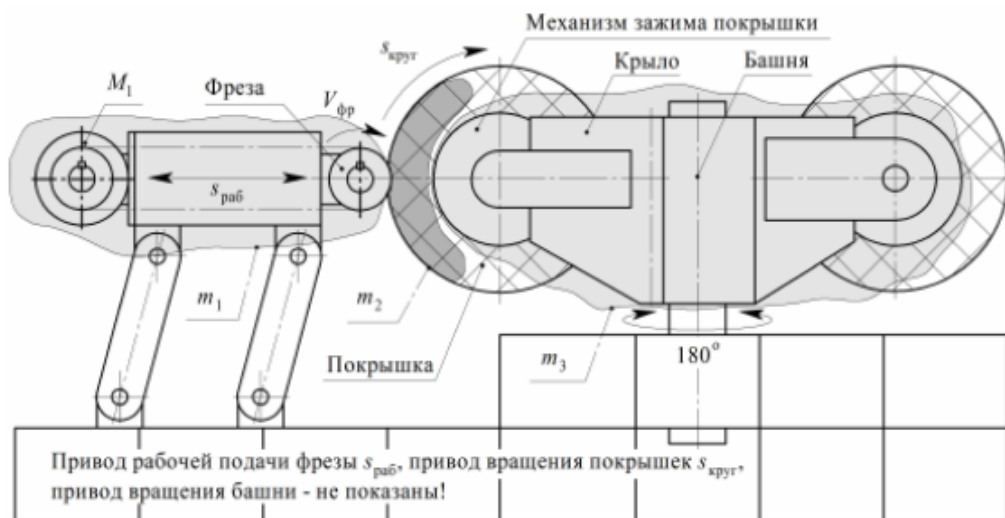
Схема оборудования для переработки шин фрезерованием [76]
